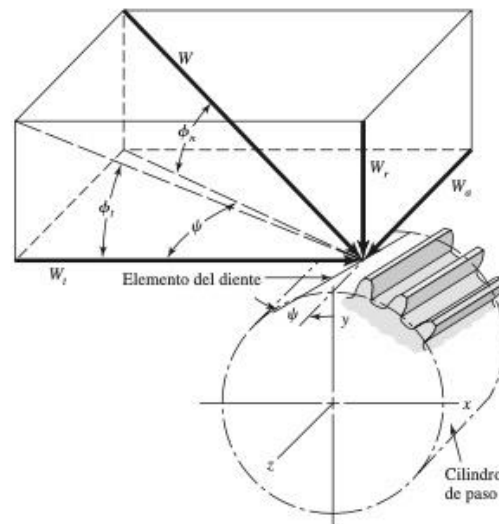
Fuerzas que actúan en los dientes de un engranaje helicoidal.
